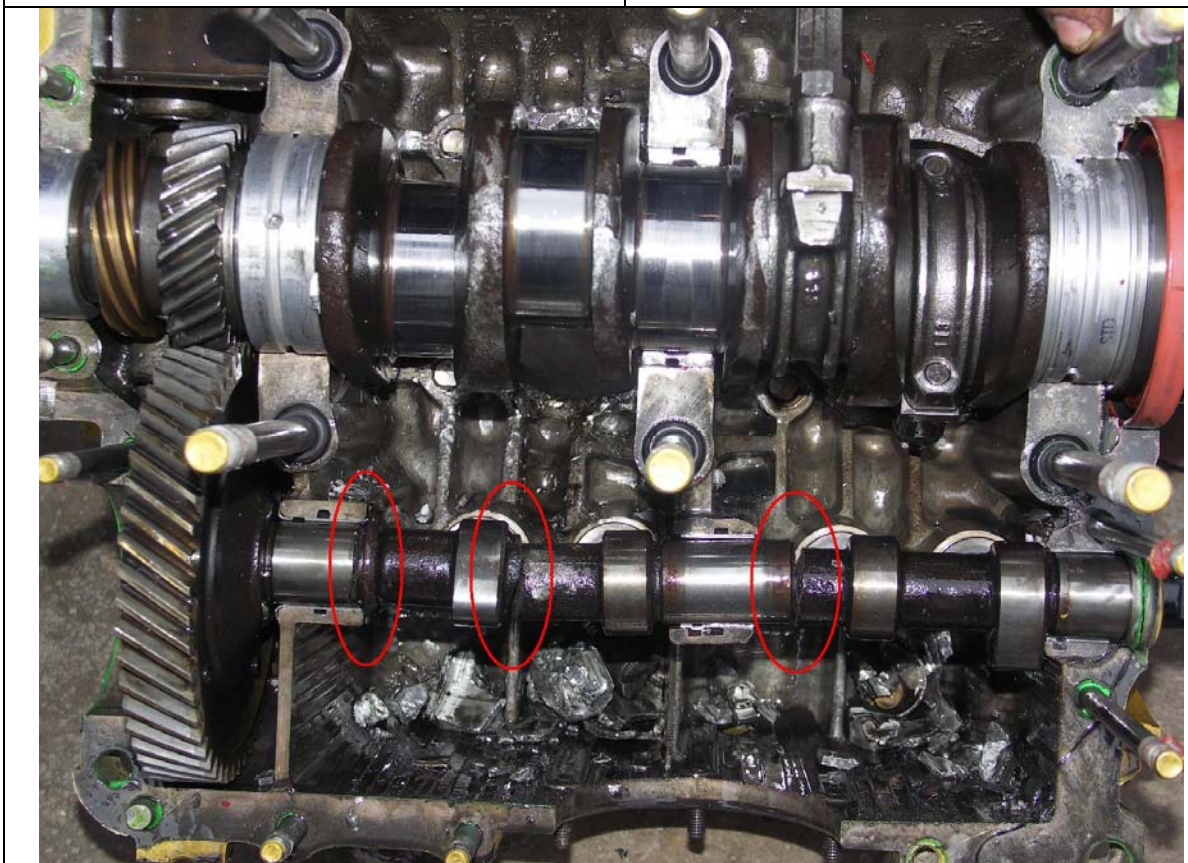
ricostruzione albero a cammes con evidenziati punti di rottura.
